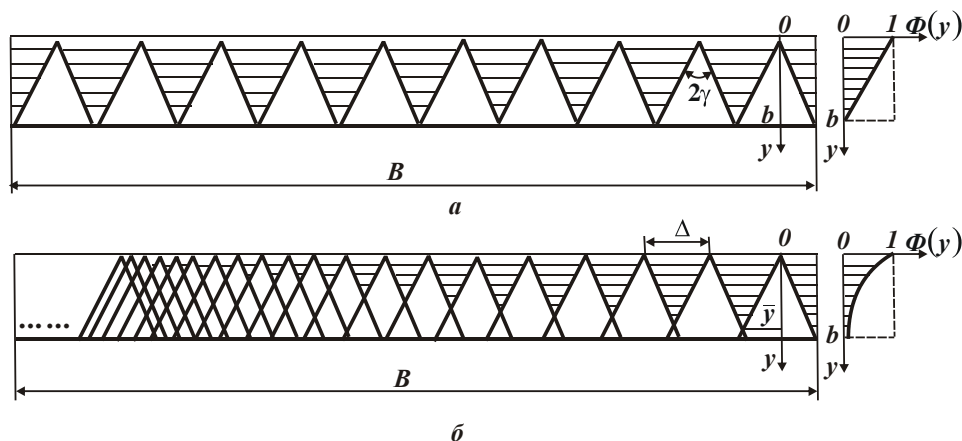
Схеми формування шорсткості поверхні при абразивній обробці.
